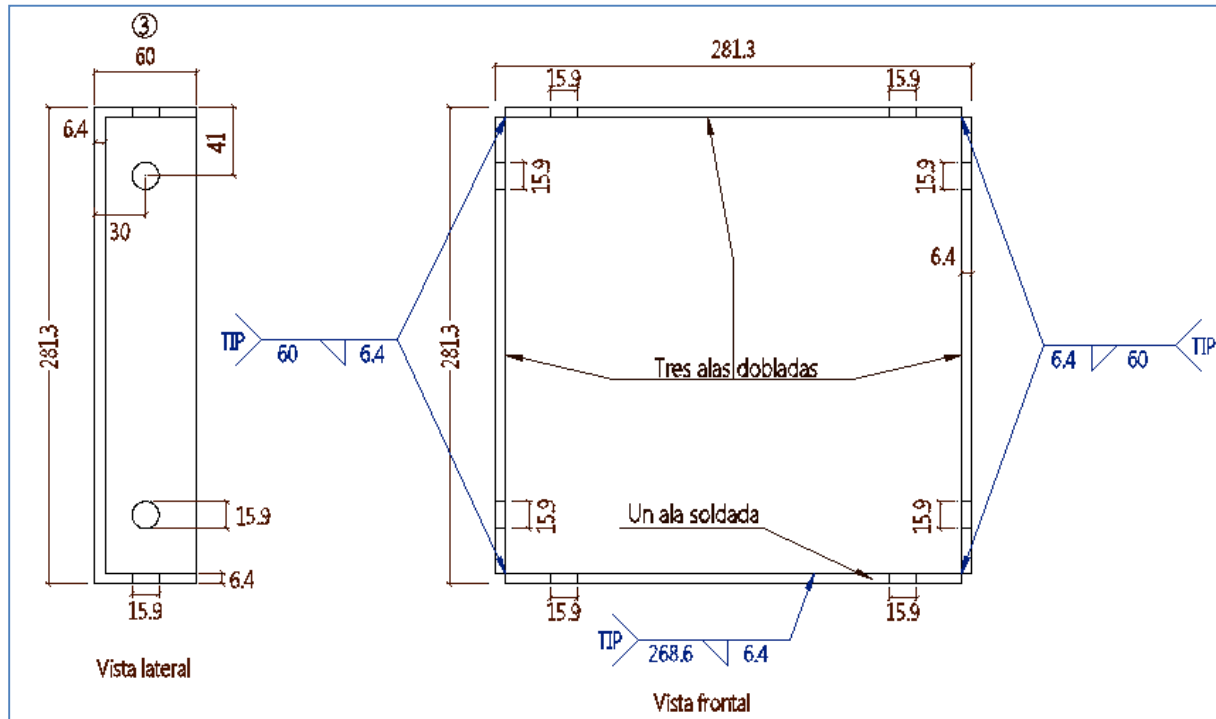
Detalle despiece pieza No.3 modelo 1 tensión.
